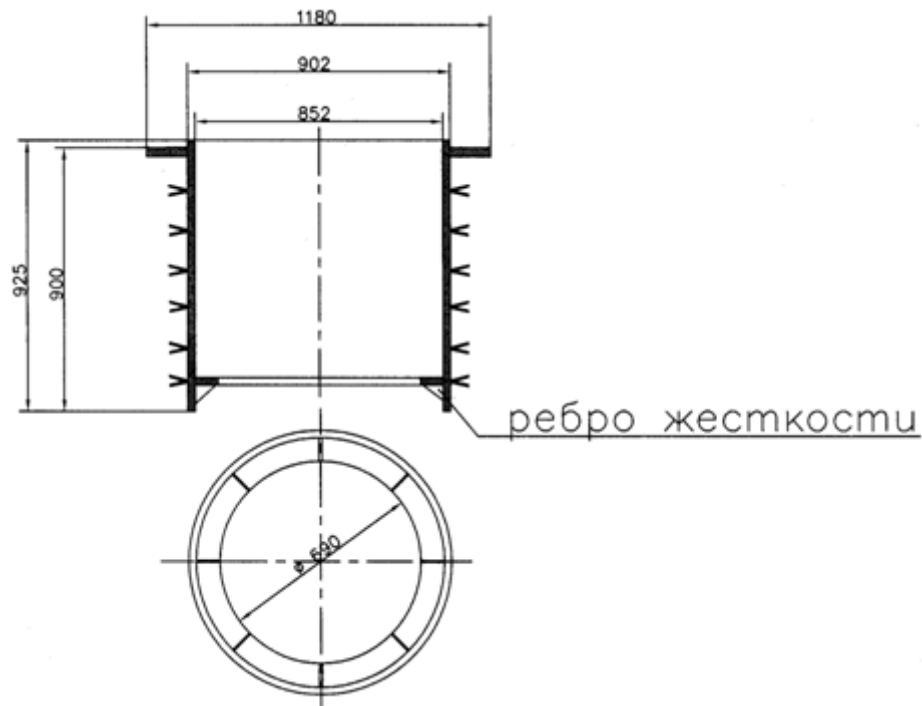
Металлоконструкция патрубков с усилением поддерживающей полочки
